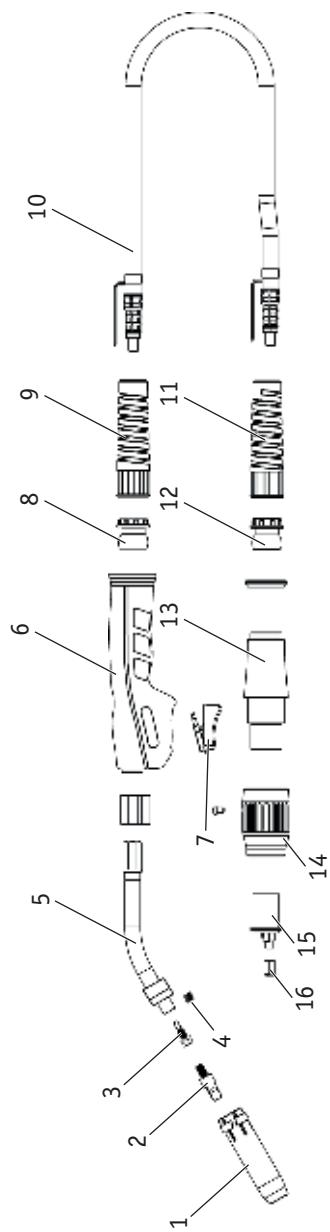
Схема горелки для МIG сварки.
